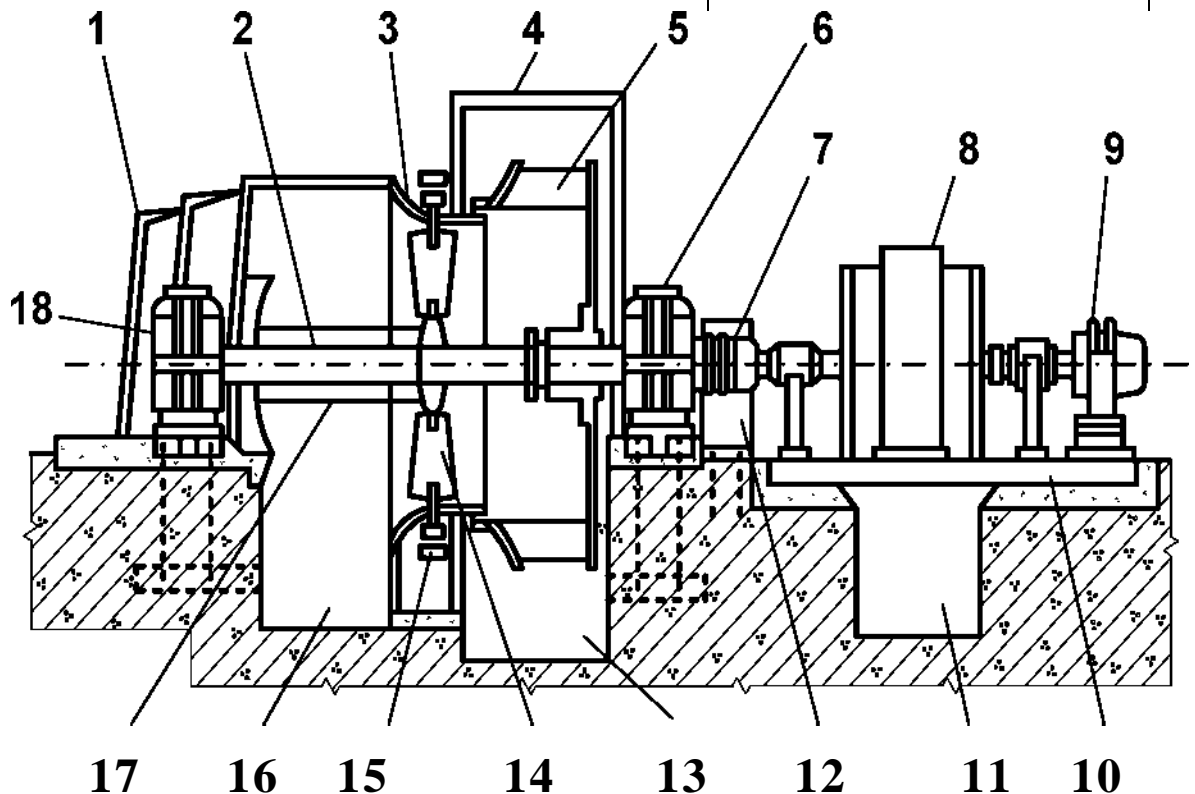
Продольное сечение вентиляторного агрегата ВЦ-31,5М: 1 - подводящий короб; 2 - вал; 3 - входной патрубок; 4 - кожух; 5 - рабочее колесо; 6 и 18 - задняя и передняя подшипниковая опора; 7 - муфта; 8 - электродвигатель; 9 - тахогенератор; 10 - рама двигателя; 11 - вентиляционный канал двигателя; 12 - ограждение муфты; 13 и 16 - отводящий и подводящий вентиляционные каналы; 14 - лопатки направляющего аппарата; 15 - механизм поворота лопаток направляющего аппарата; 17 - связь (спица)
